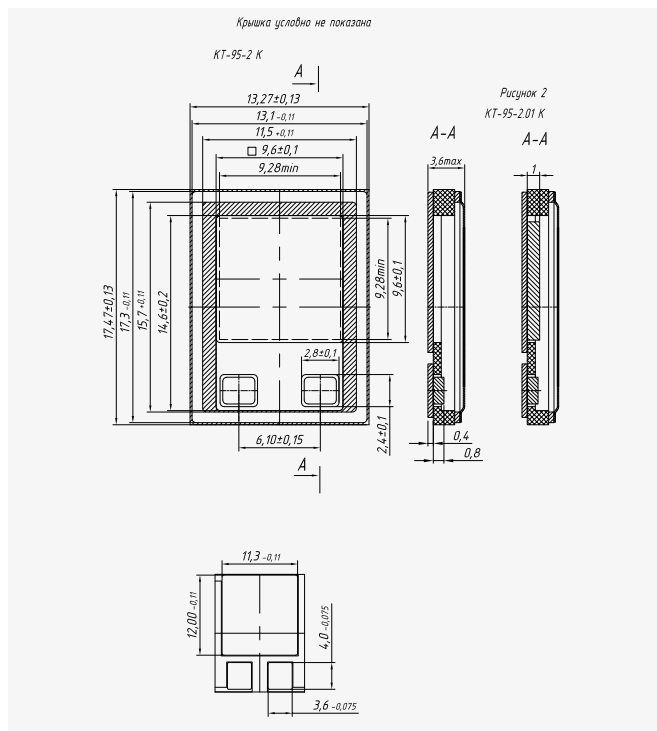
Габаритный чертеж металлокерамического корпуса KT-95-2 K
